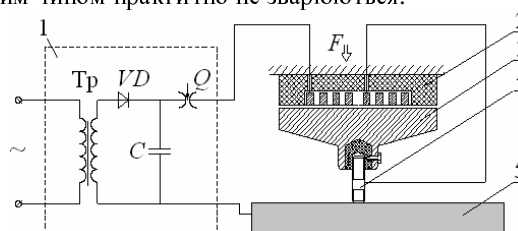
Принципова схема ударно-конденсаторного зварювання з магнітно-імпульсним приводом: 1 – генератор імпульсних струмів; 2 – дисковий індуктор; 3 – штовхач; 4 – зварювана деталь; 5 – корпусна деталь; F – зусилля притискування деталей
